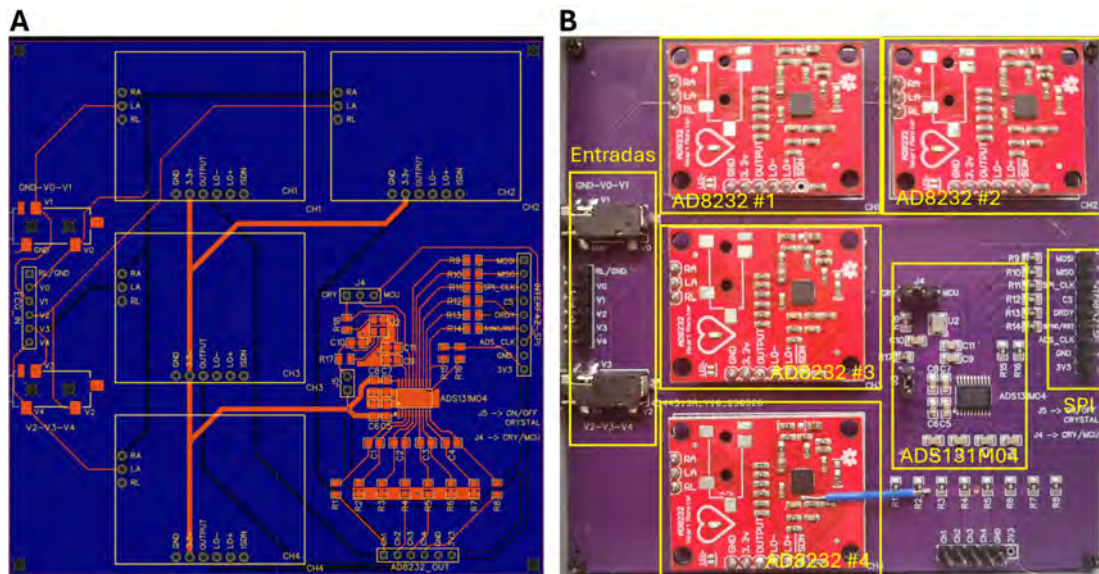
Vista general del diseño de la PCB para el simulador de aECG de cuatro canales. (A) Diseño en software de la PCB. (B) Implementación física de la PCB.
